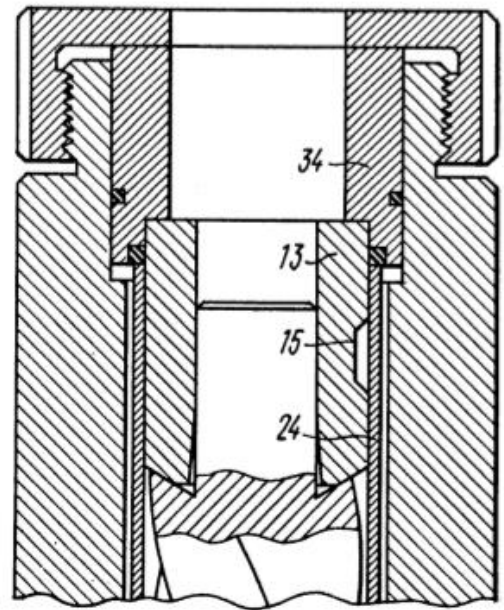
eine Teilansicht einer Vorrichtung zur Herstellung des Rotors unter gleichzeitigem Einpressen einer Kupplung im Längsschnitt
